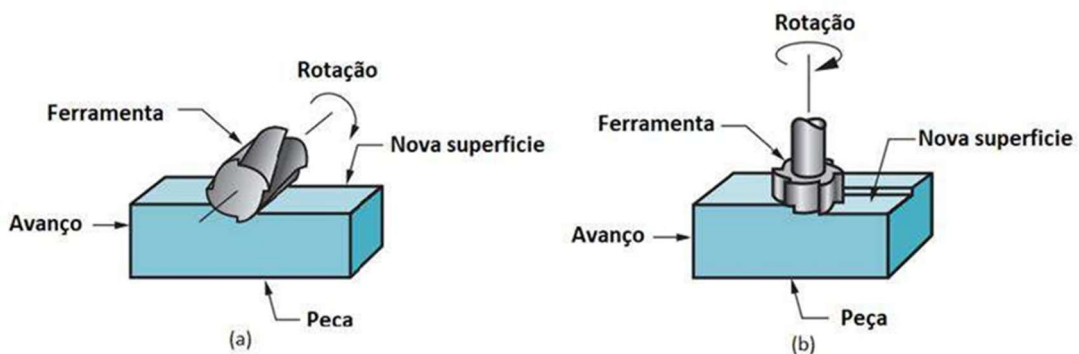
Fresagem periférica (a), fresagem de topo (b), adaptado de [8].
